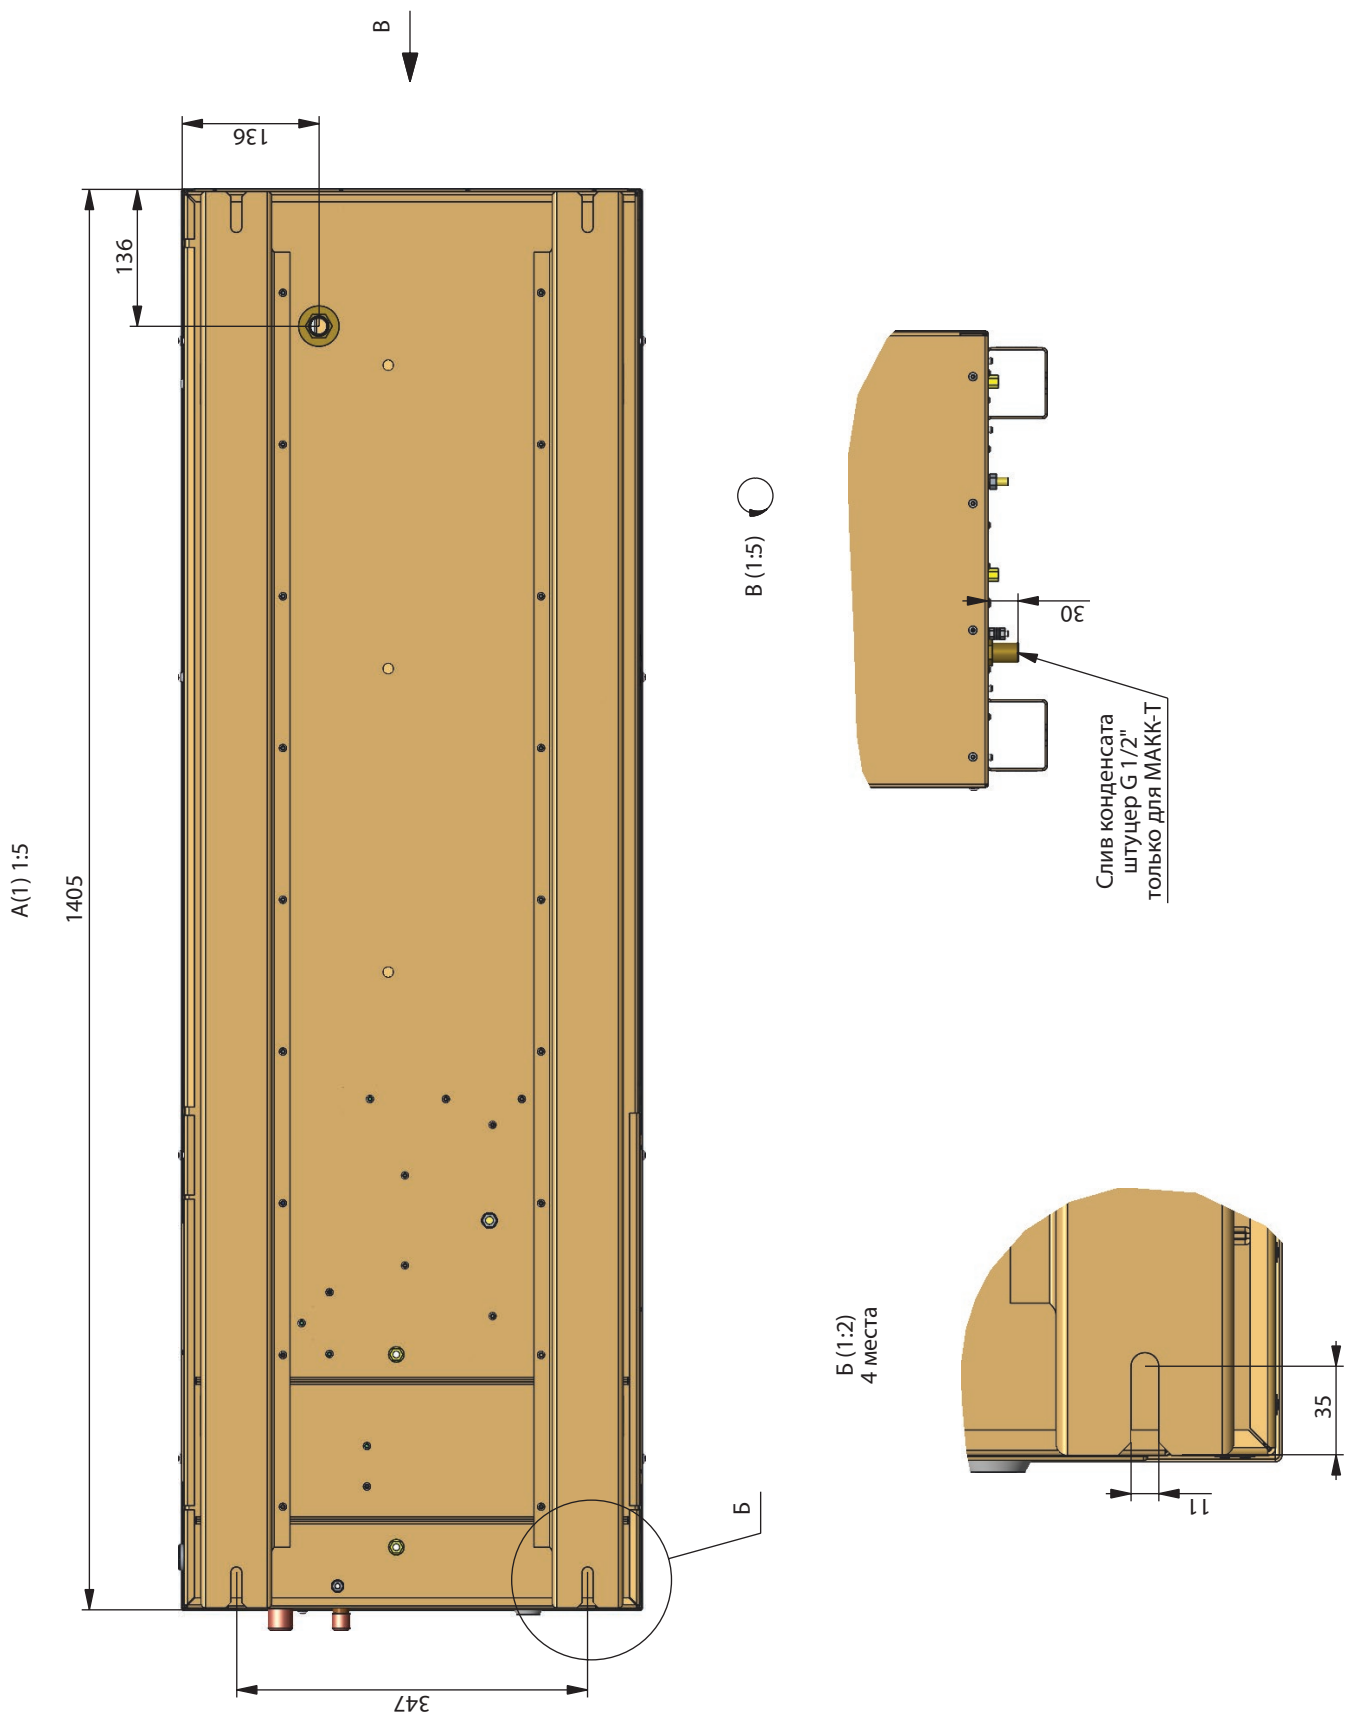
Агрегат компрессорный типа МАКК 310-181, -211
